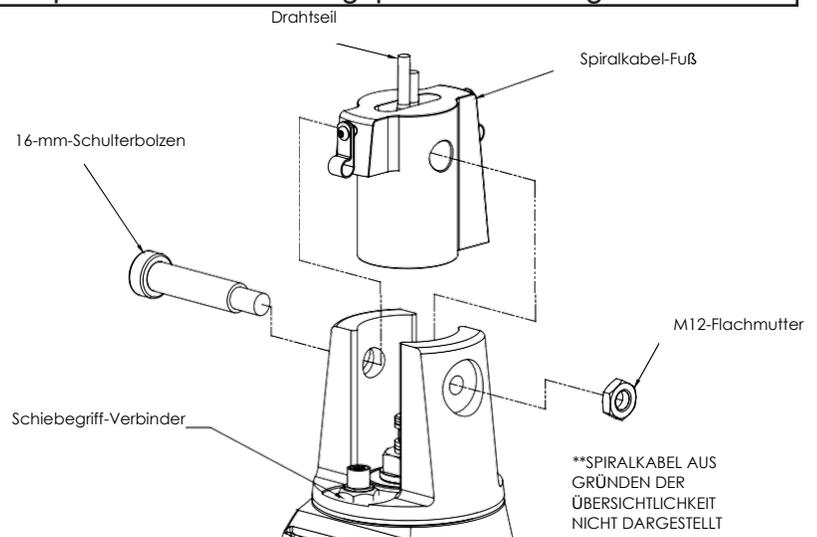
Abb. M Entfernen des Drahtseils vom Schiebegriff/G360™.
